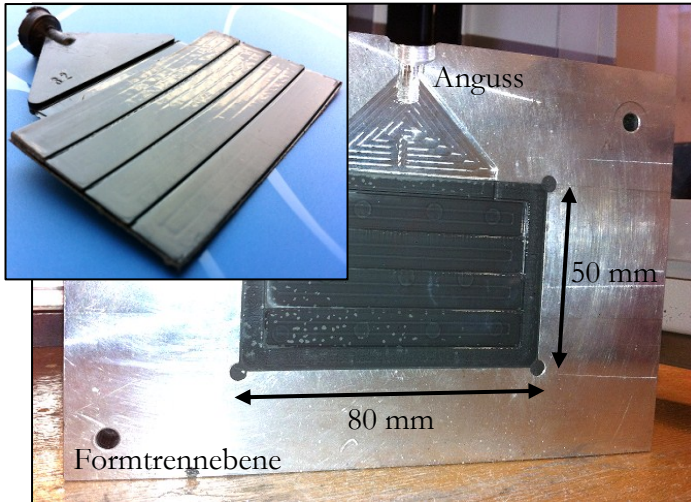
Spritzgusswerkzeug (SG-WZ) mit Quarzglasformeinsatz und abgeformtes Stufenteil
